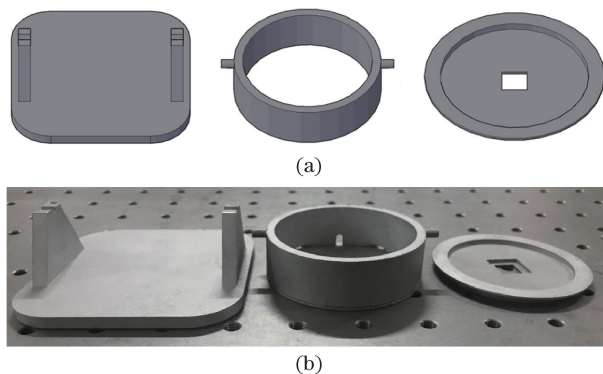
定点旋转平台。(a) CAD 图;(b)实物图
